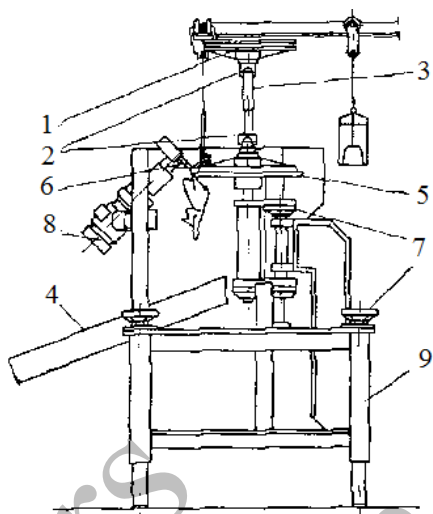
Mașină pentru detașat picioare: 1- roată ghidare conveier; 2- cuplaje cardanice; 3- cuplaj telescopic; 4- plan înclinat; 5- roată cu pinteni; 6- cuțit disc; 7- mecanism reglare; 8- motor electric; 9- cadru mașină
